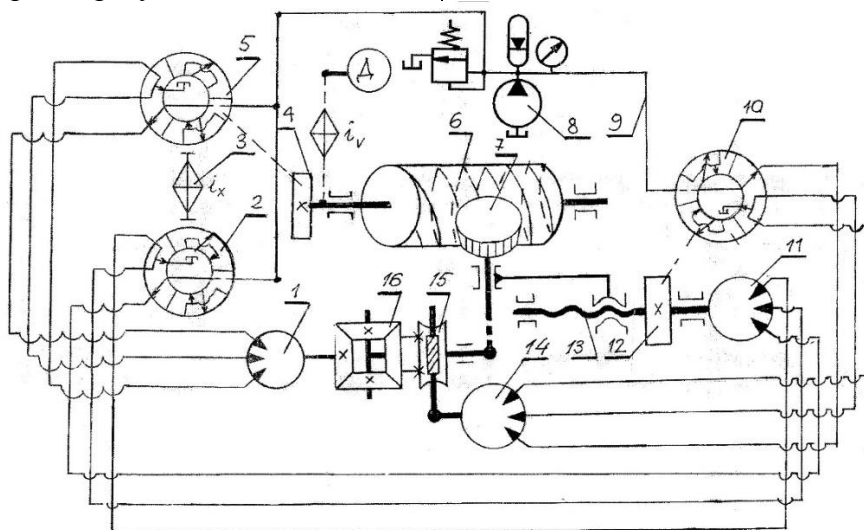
Структурная схема резьбонарезного станка с гидравлическими формообразующими связями для нарезания цилиндрических червяков обкатным резцом (долбяком)
